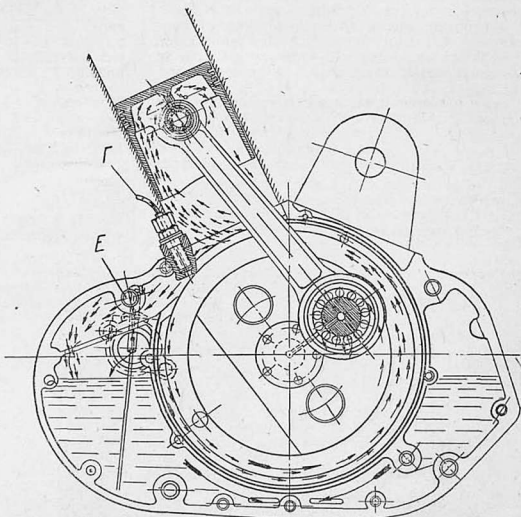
Схема смазки двигателя AM-600 (продольный разрез). Г—штуцер смазки направляющей клапана; Е—указатель уровня масла
